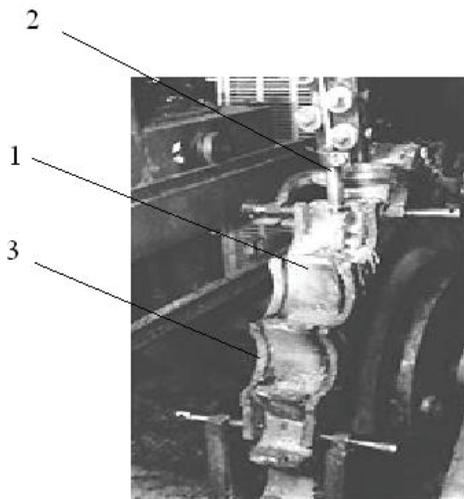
Наплавка ведущей звездочки бульдозера:
